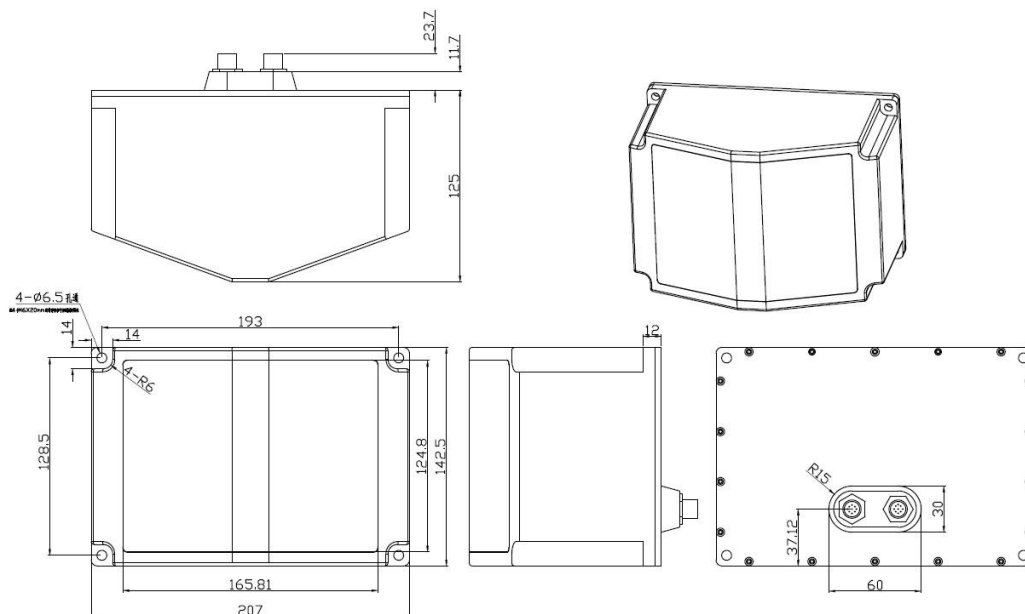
CH128 激光雷达后面出线的外形尺寸图
